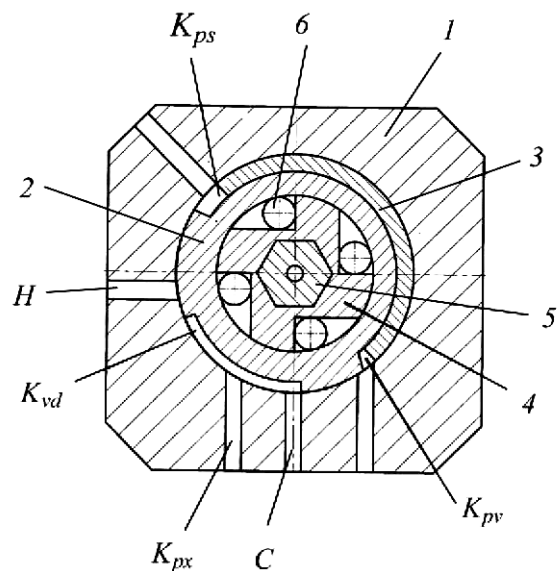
Схема поворотного двигателя гидравлического перфоратора: 1 — корпус; 2 — поворотная втулка; 3 — статор; 4 — ротор; 5 — буровая штанга; 6 — ролик
